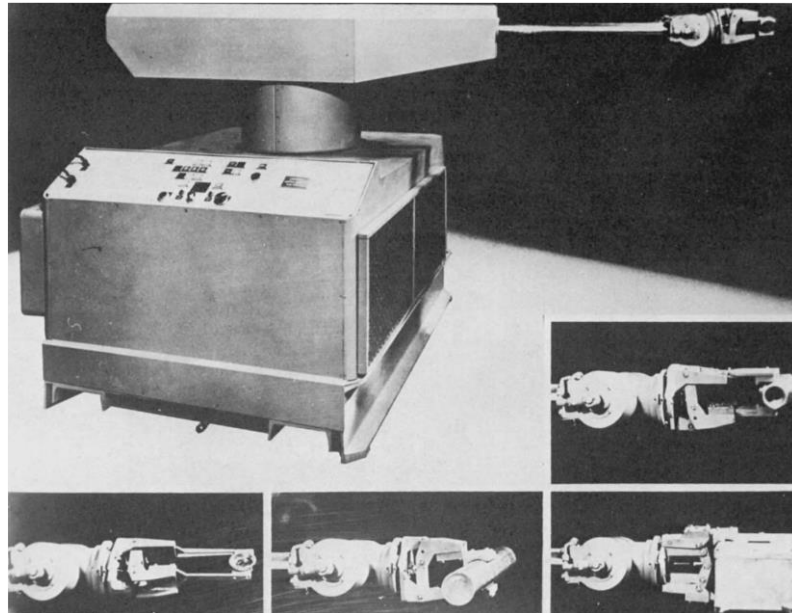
Primeira instalação do robô (máquina de fundição sob pressão numa fábrica da General Motors) [14]
